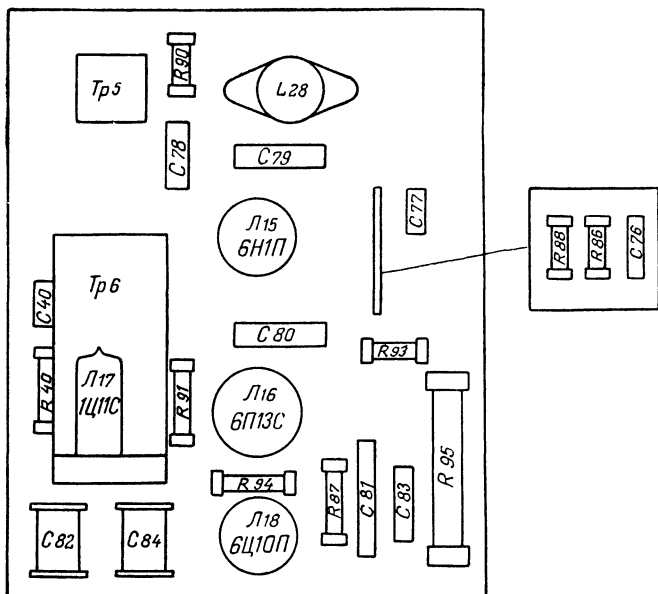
Расположение деталей на плате строчной развертки телевизора „Старт“.
